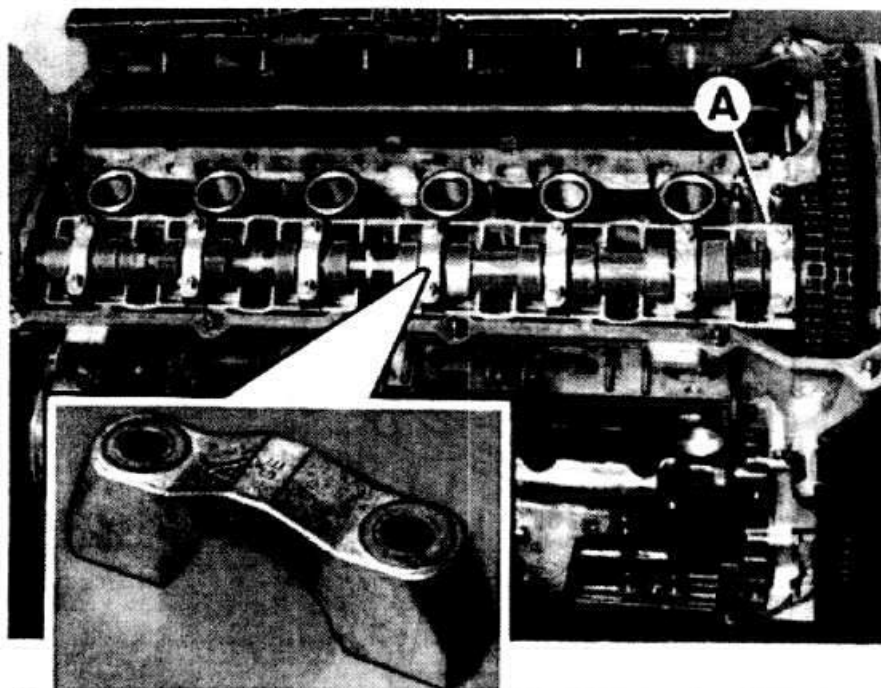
Маркировка держателей и корпусов подшипников распределительных валов
